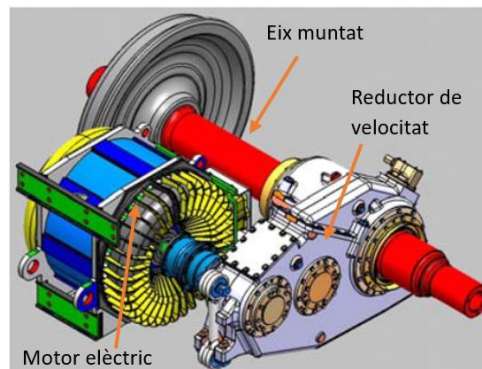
Conjunt de motor i reductor del fabricant Alstom.
